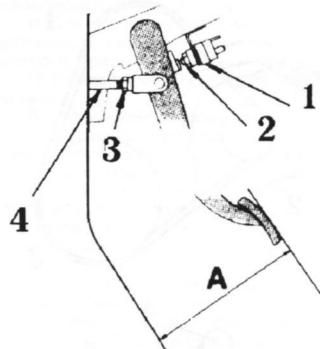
а Подробности регулировки высоты педали тормоза
